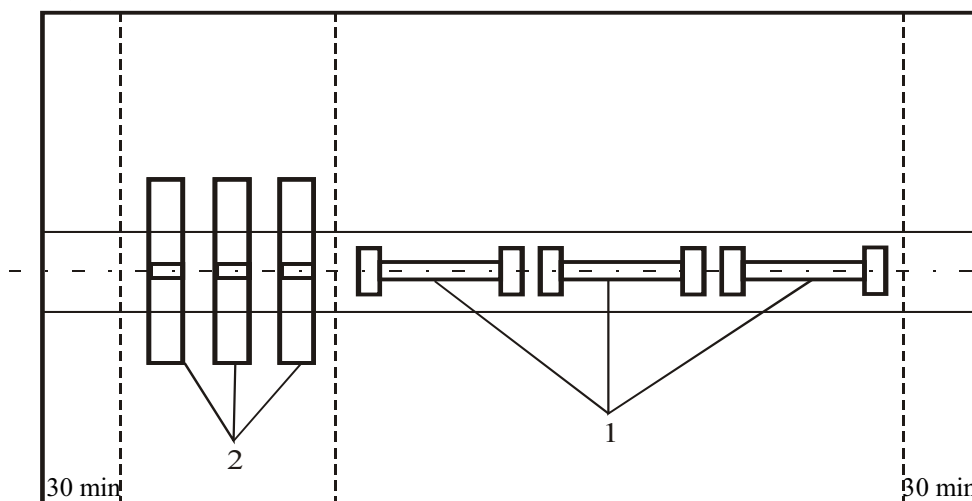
Схема вырезки образцов для механических испытаний наплавленного металла:
